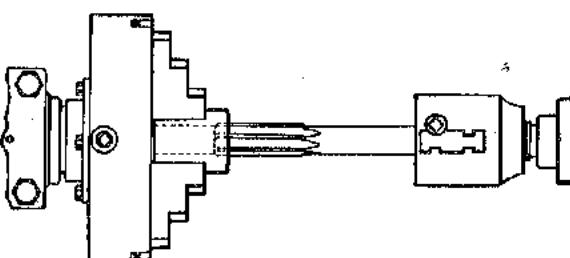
Los escariadores pequeños de mango cilíndrico pueden sujetarse en un portabrocas (South Bend Lathe Co.)
